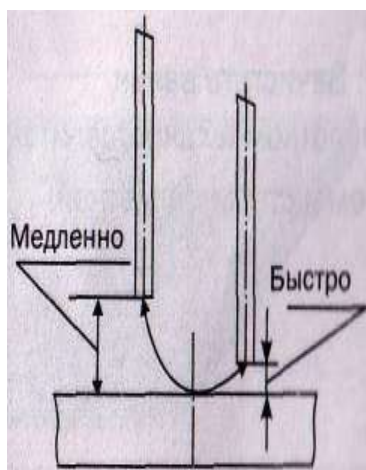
Способы зажигания сварочной дуги.
